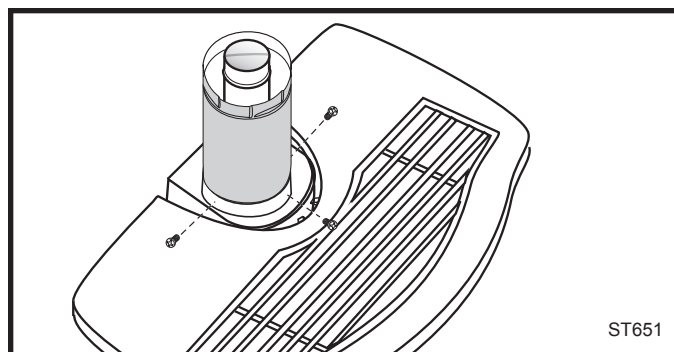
Installation du conduit de raccordement extérieur DuraVent.
